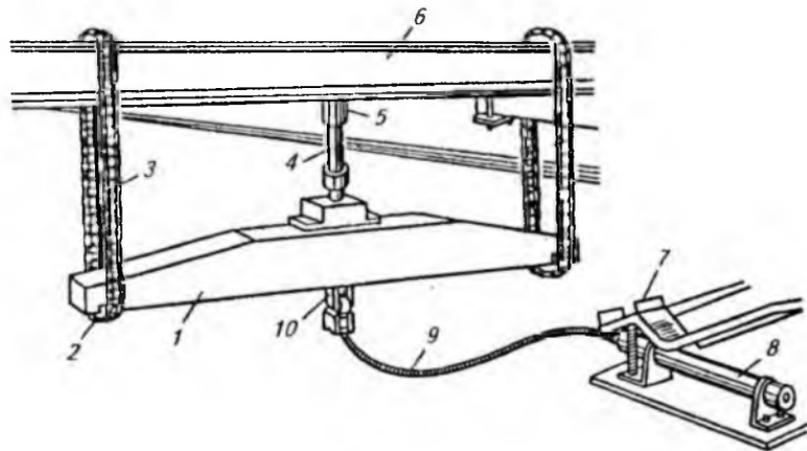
Гидравлическое приспособление для правки рамы:
